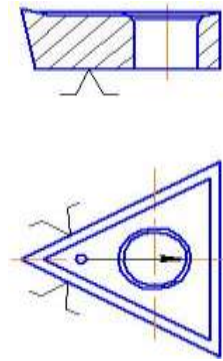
Схема базирования и закрепления СМП
